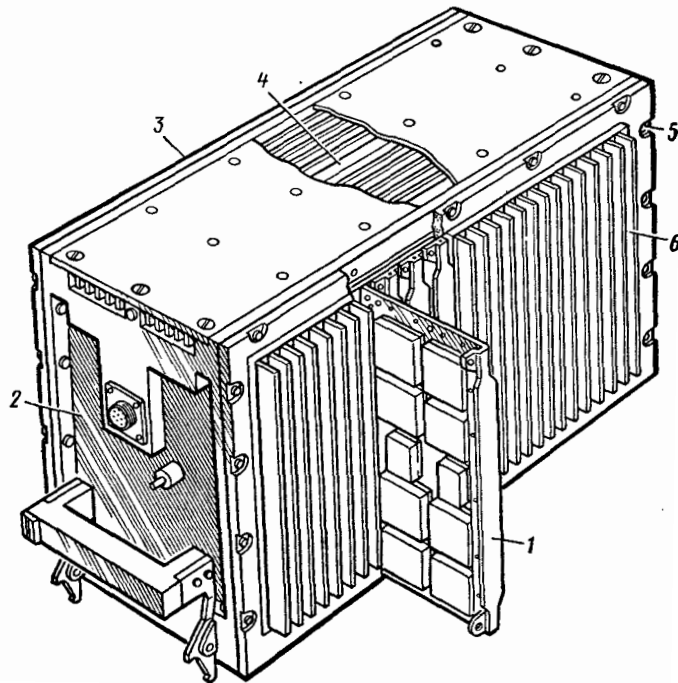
Герметичный блок РЭА разъемной конструкции:
